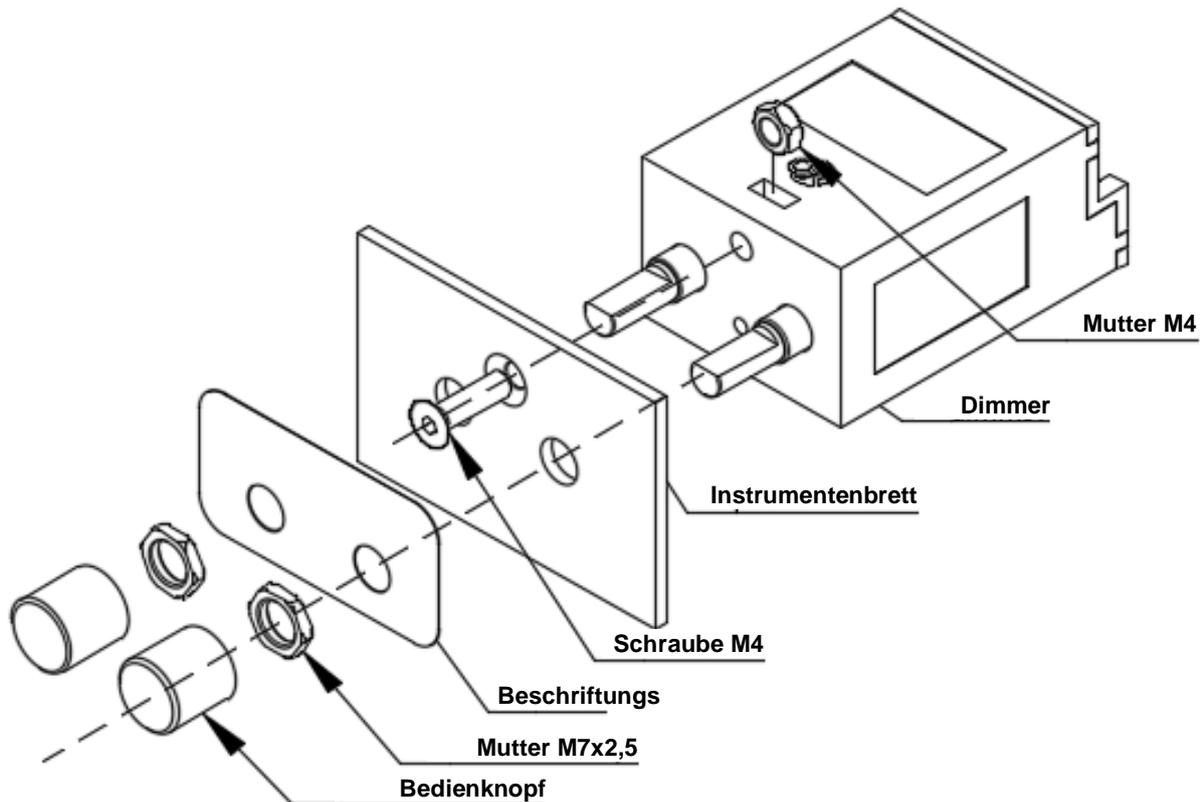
Explosionszeichnung für den Einbau des Dimmers in das Instrumentenbrett
